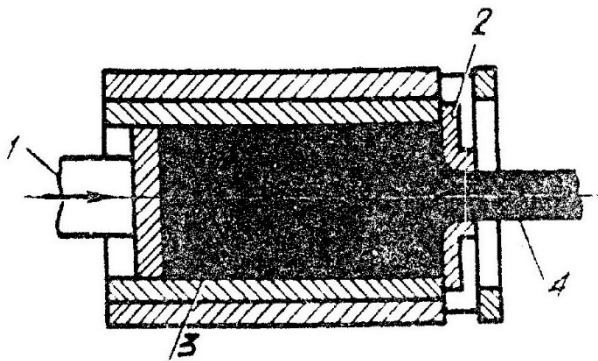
Схема пресування: 1 - пуансон; 2 - матриця; 3 - пресована заготовка; 4 - пруток
